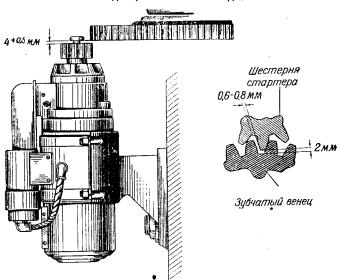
Установочные зазоры между шестерней стартера и зубчатым венцом первичного привода вентиляторов
